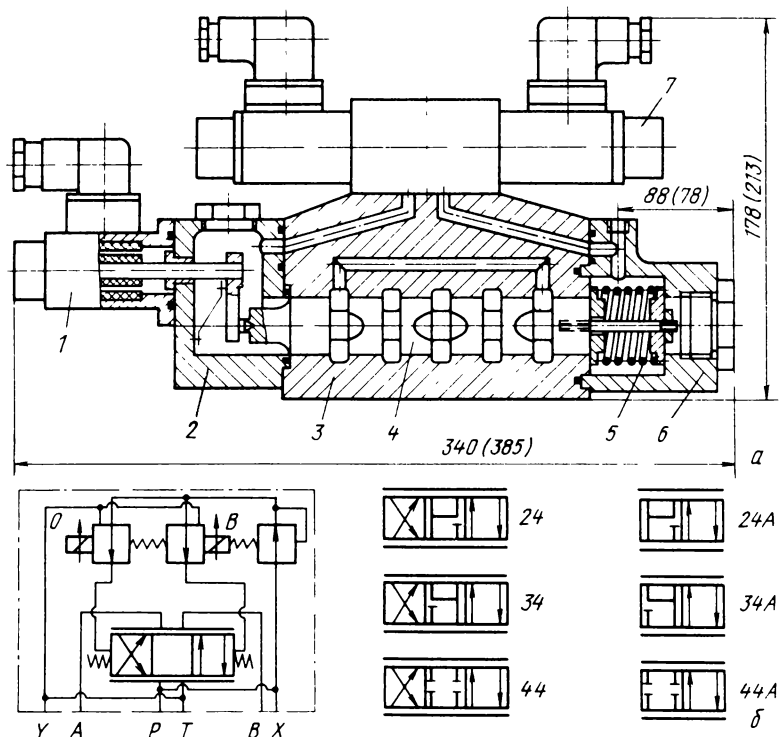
Конструкция, размеры (а) и гидравлические схемы (б) гидрораспределителей с пропорциональным управлением РП16 и РП20 (размеры в скобках)
